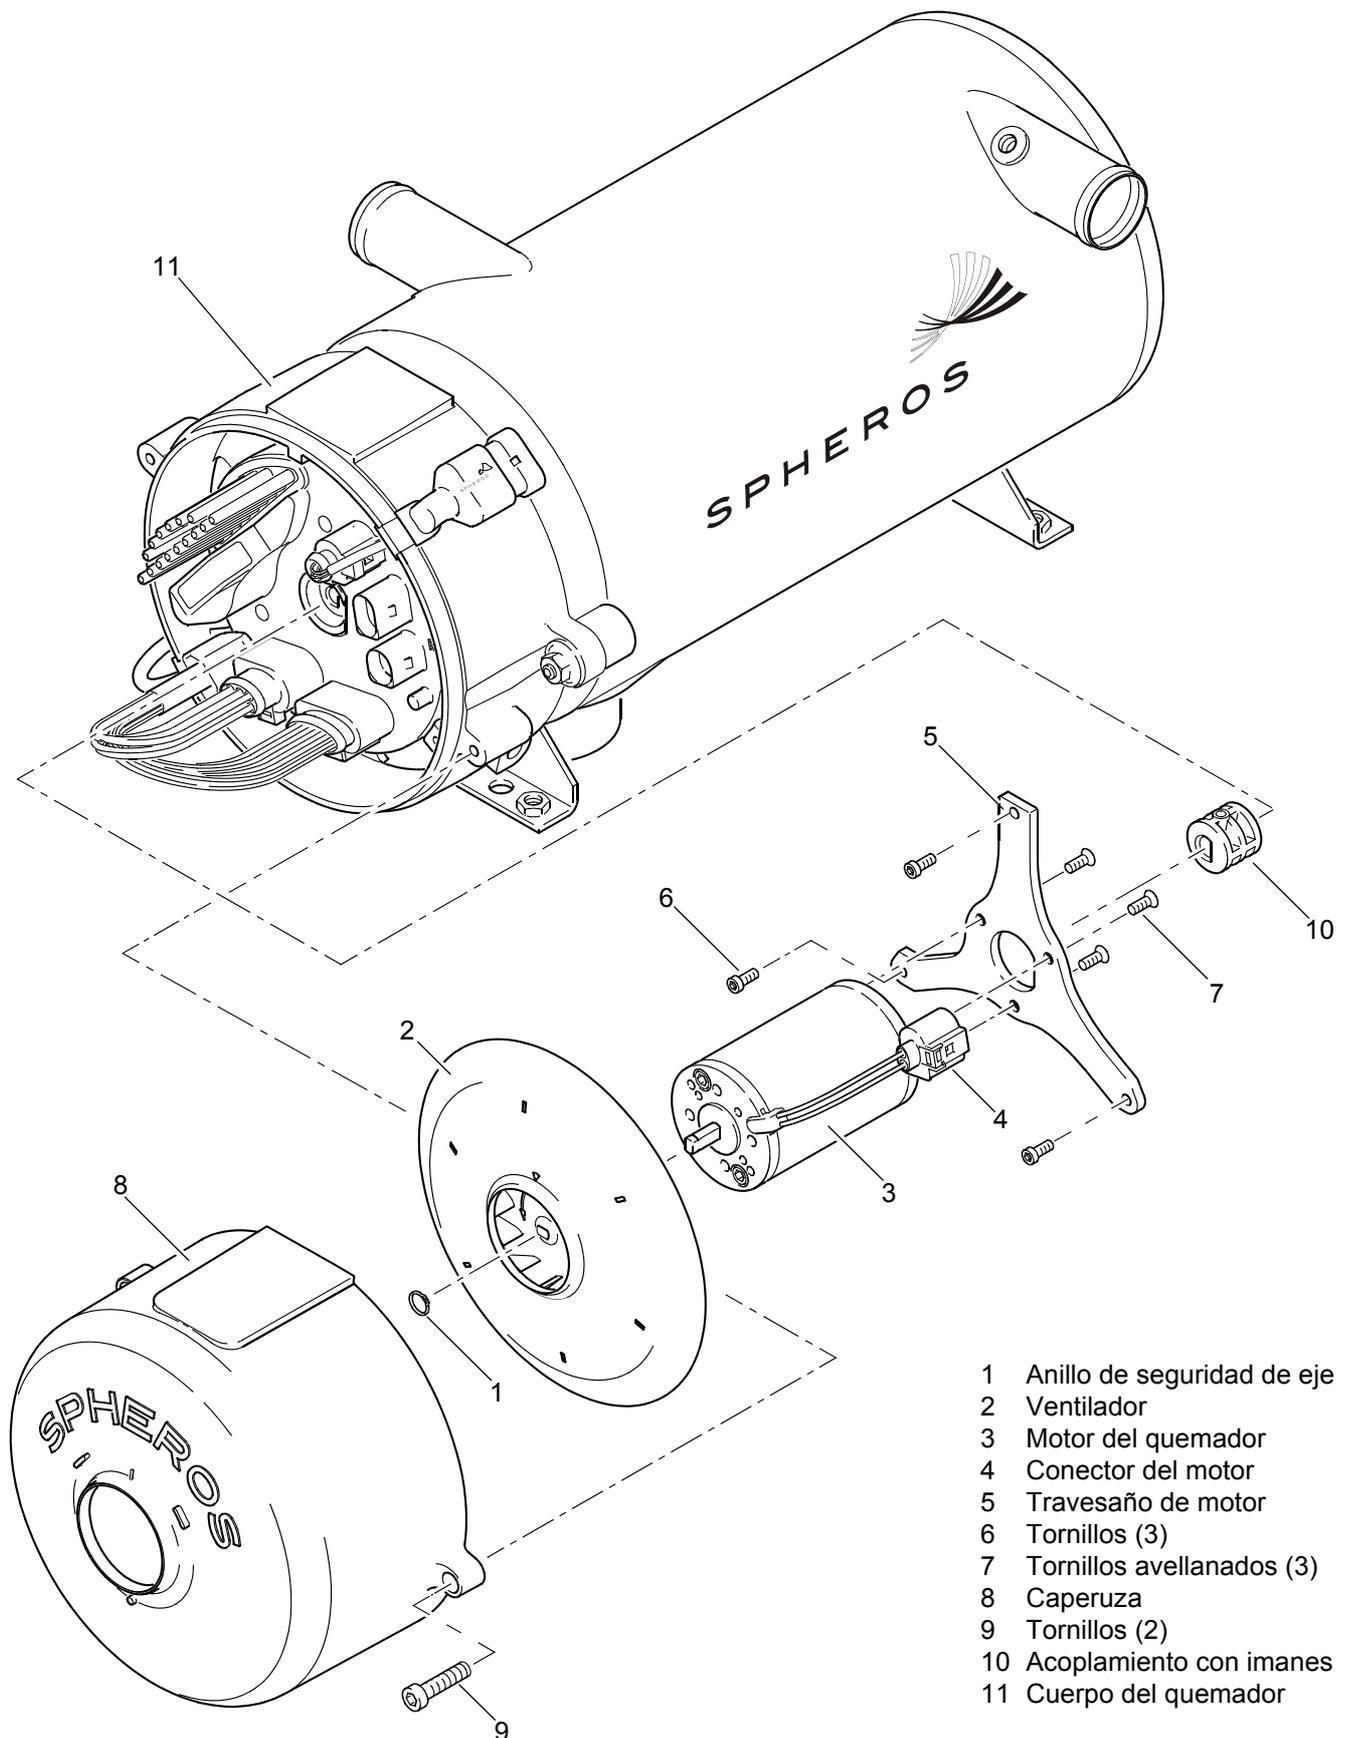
Montaje y desmontaje del ventilador de aire de combustión
